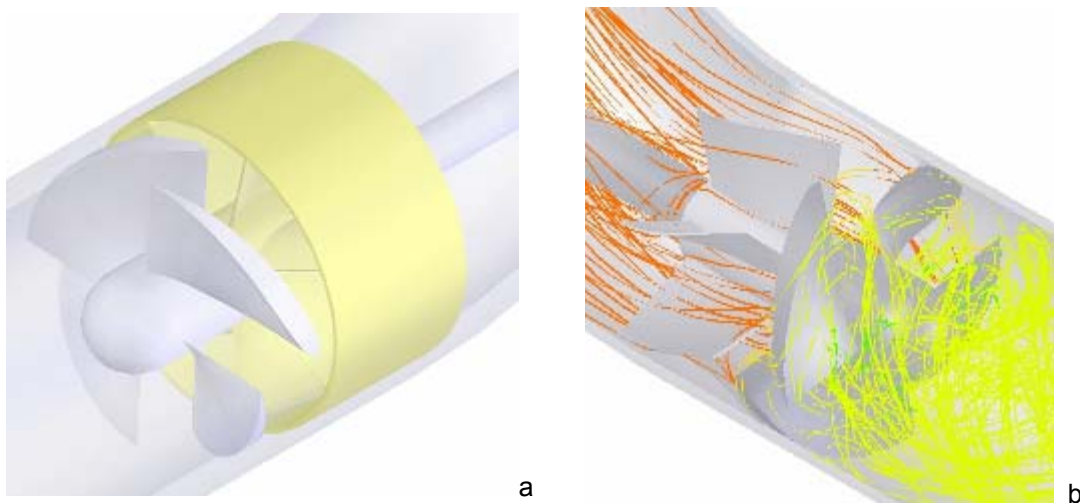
a) Diseño del rotor y estator de la máquina hidráulica.
